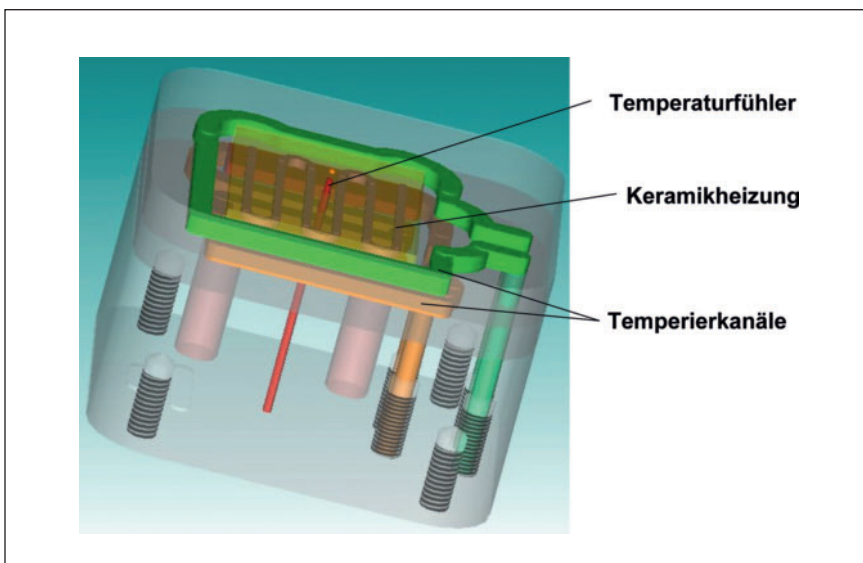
Werkzeugzeugsatz mit integrierter Keramikheizung (Bild: GWK Gesellschaft Wärme Kältetechnik mbH, Kierspe)
